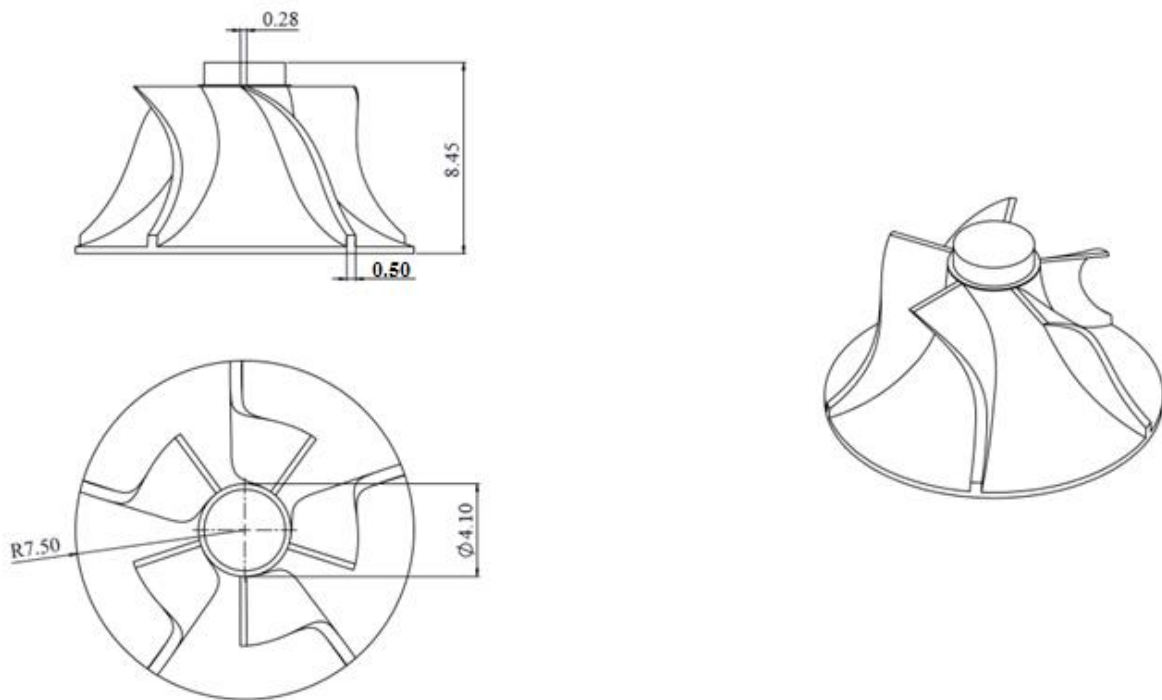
CAD dimensiones (cm) rotor 5 álabes.
